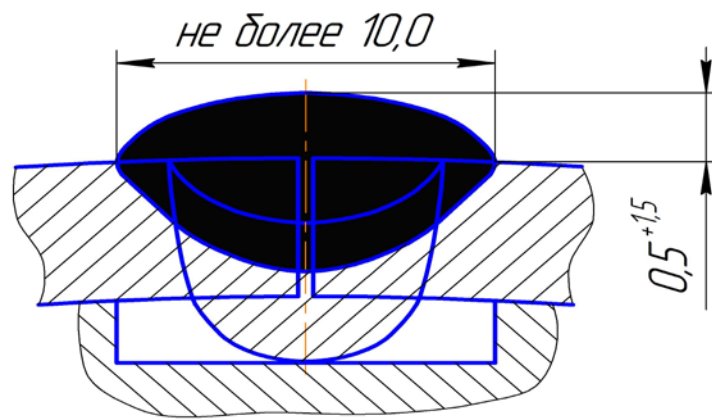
Эскиз конструктивных элементов продольного сварного шва цилиндра после сварки второго прохода
